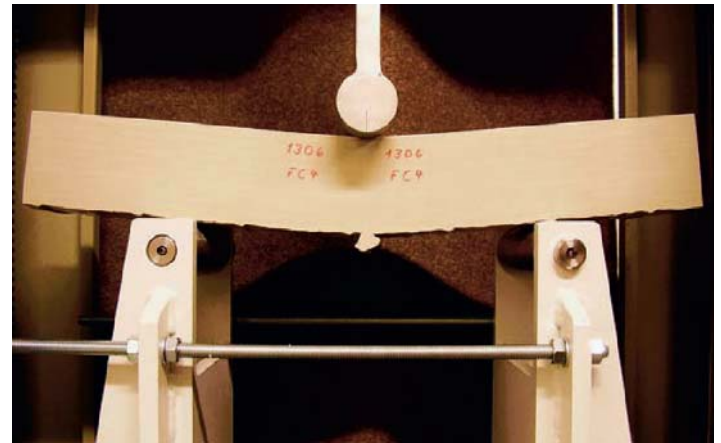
Technologischer Biegeversuch an einem geschweißten Probekörper mit einer Wanddicke von 100 mm [Quelle: Hessel Ingenieurtechnik GmbH]
